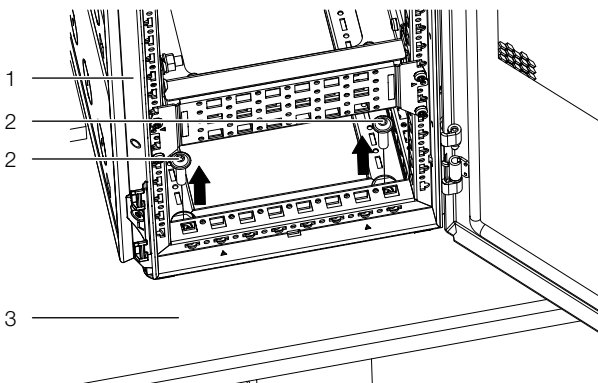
Transportbefestigung hinten (2 x Schrauben)
